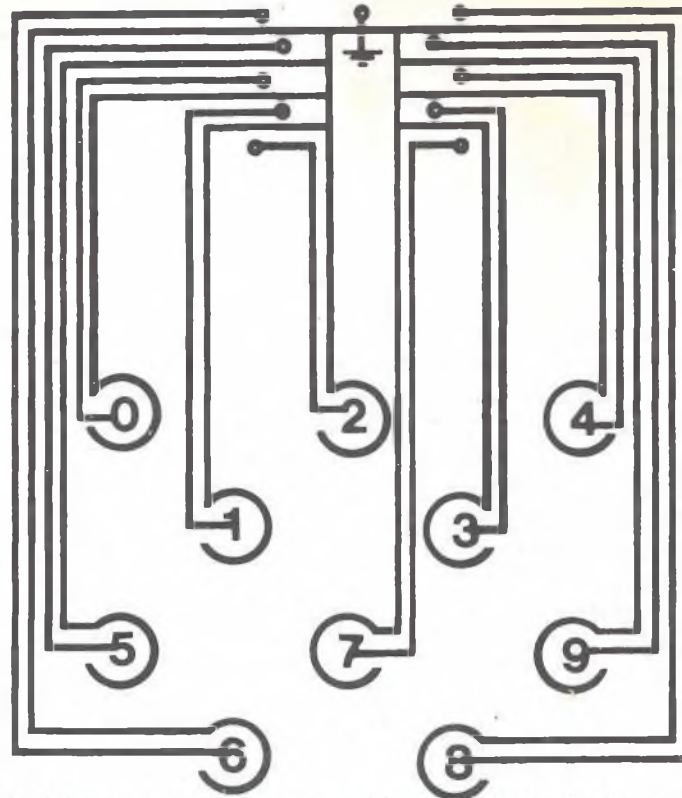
Sugestão de lay-out para a montagem do teclado à partir de uma placa de circuito impresso (ver texto).
